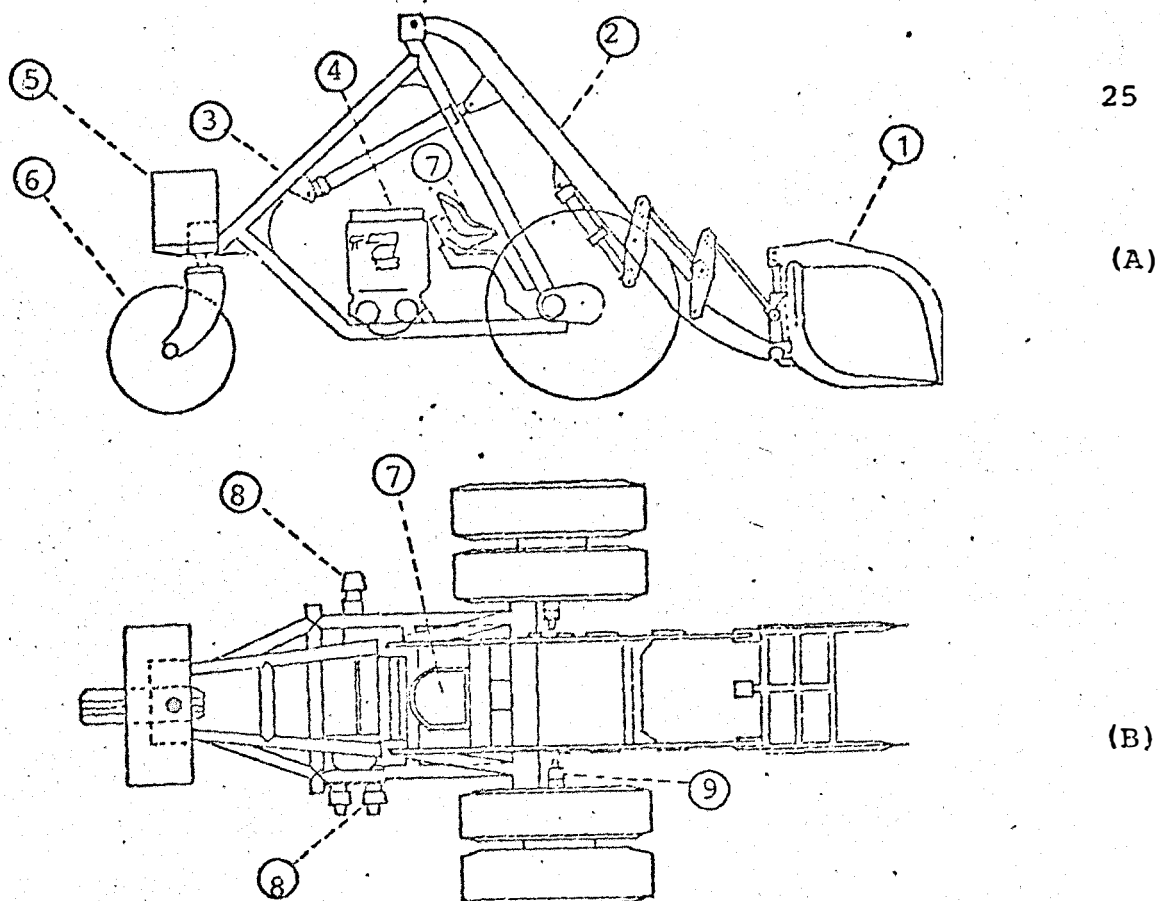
Esquema da carregadora. A) Vista lateral e B) Vista de cima: 1) garra; 2) lança; 3) chassi; 4) motor Diesel; 5) Depósitos de combustível e óleo hidráulico; 6) roda pivotada; 7) assento do operador; 8) motores hidráulicos e 9) transmissão hidráulica.
